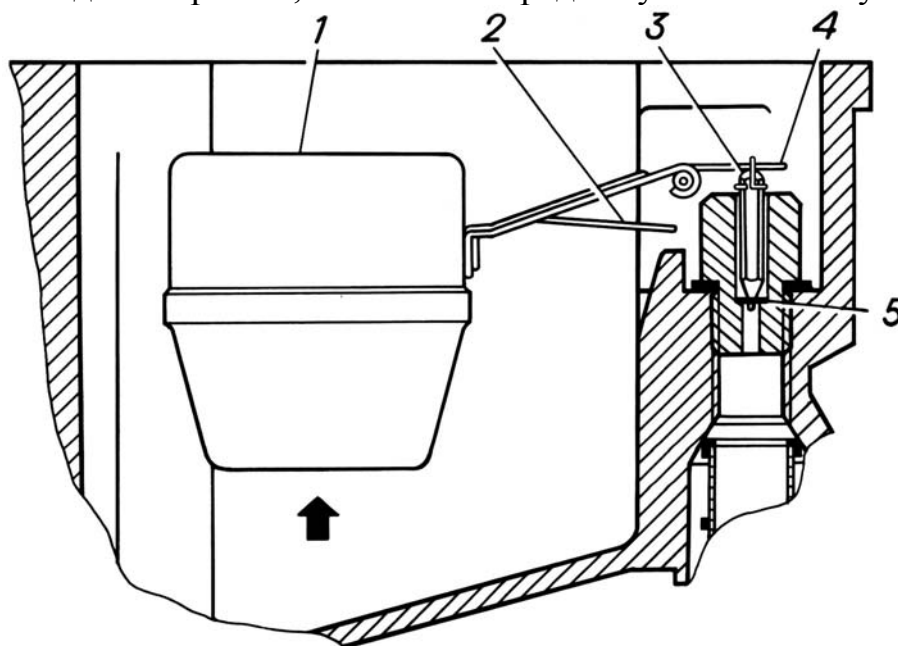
Регулировка поплавкового механизма: 1 - поплавок; 2 - язычок для регулировки хода клапана; 3 - клапан; 4 - язычок для регулировки уровня топлива; 5 - уплотнительная шайба
